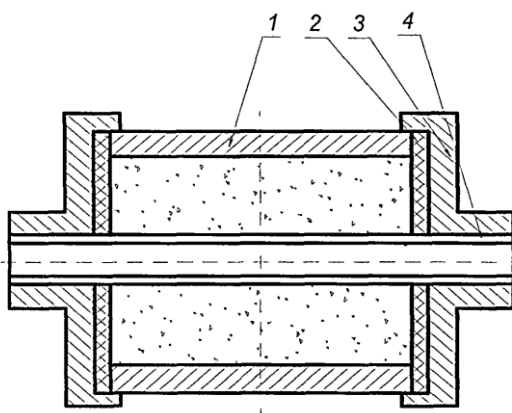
Схема опковки для відцентрового заливання: 1 - заготовка-основа;
